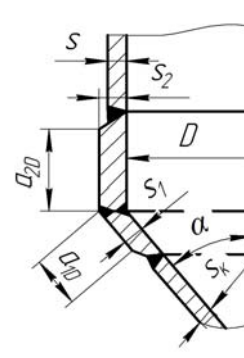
Розрахункова схема переходу між циліндричною та конічною обичайкою
